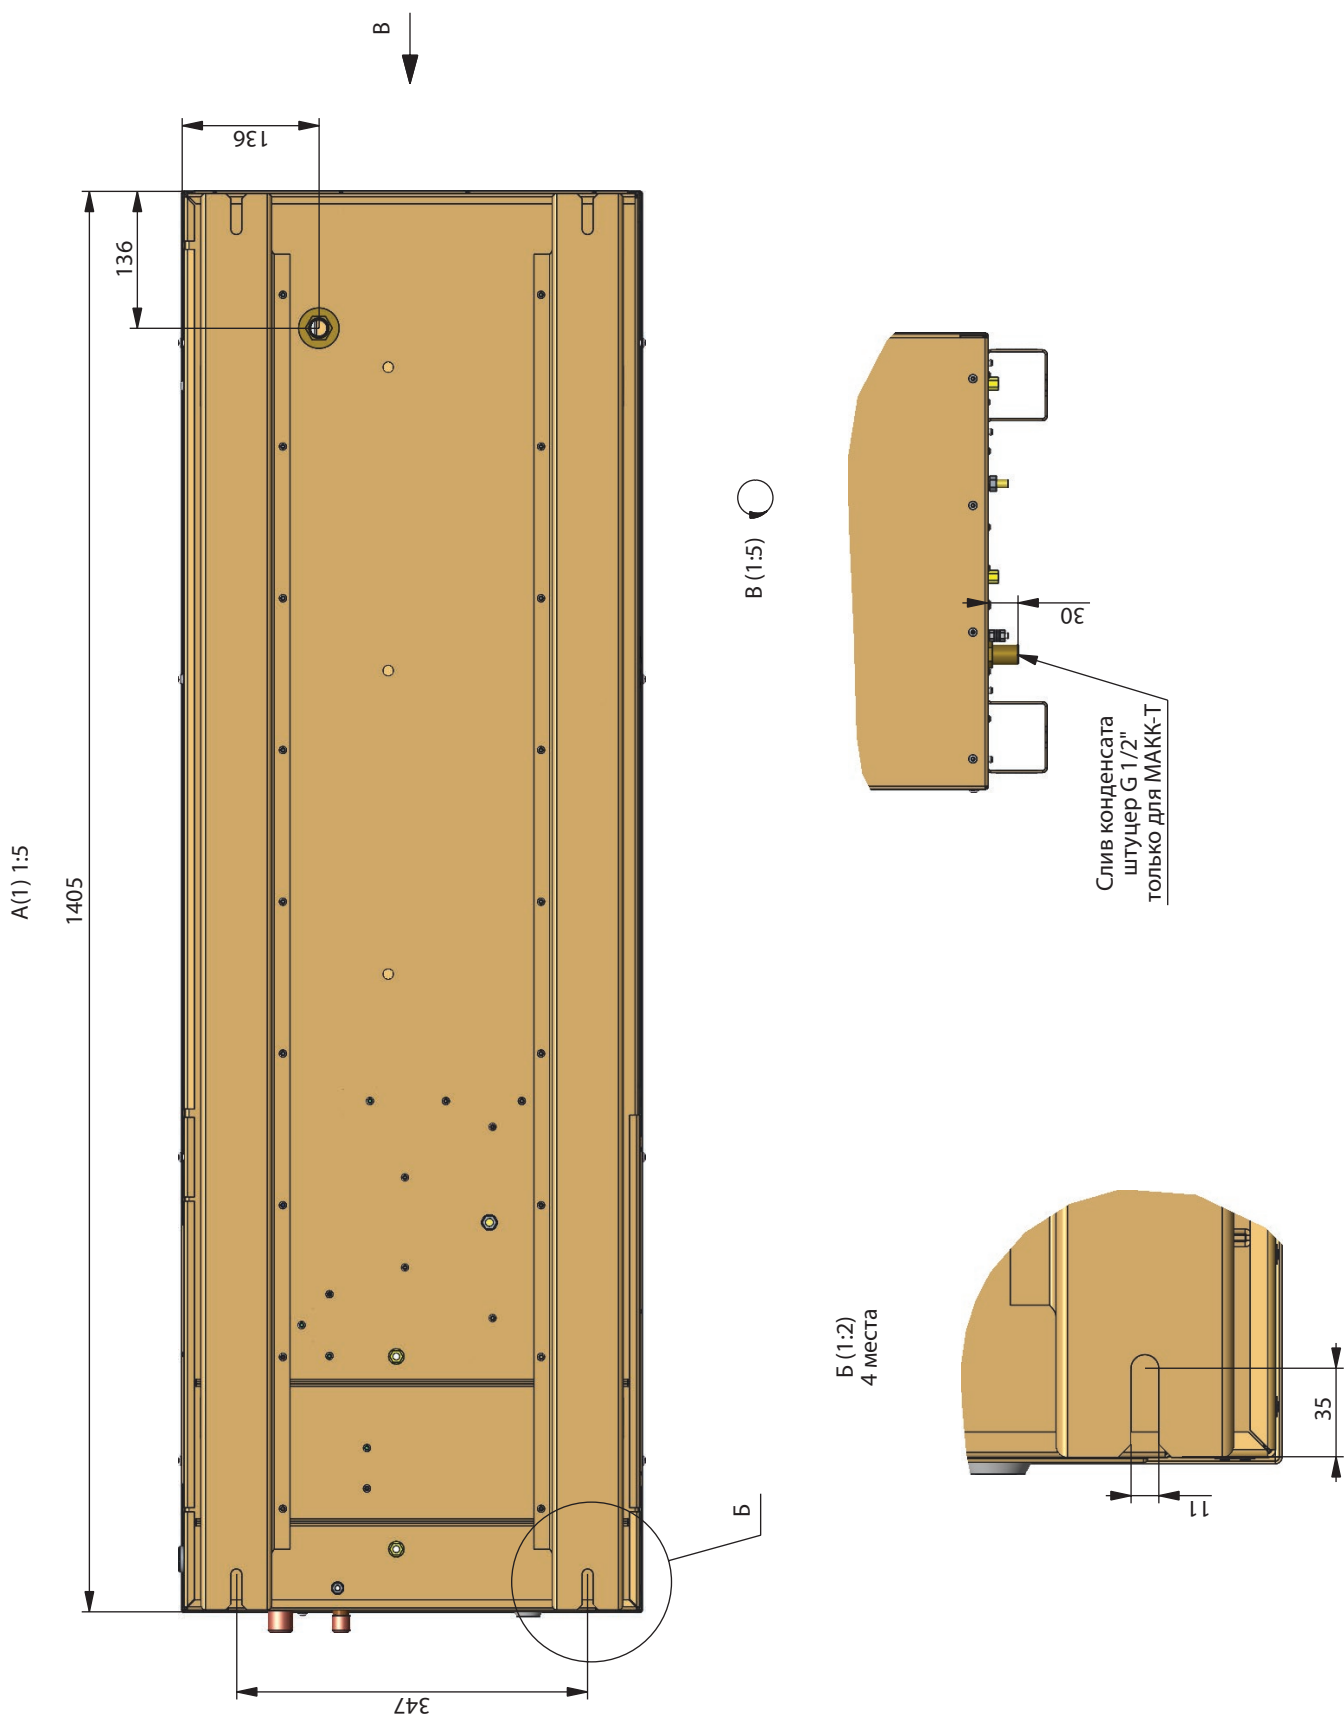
Агрегат компрессорный типа МАКК 110-201
